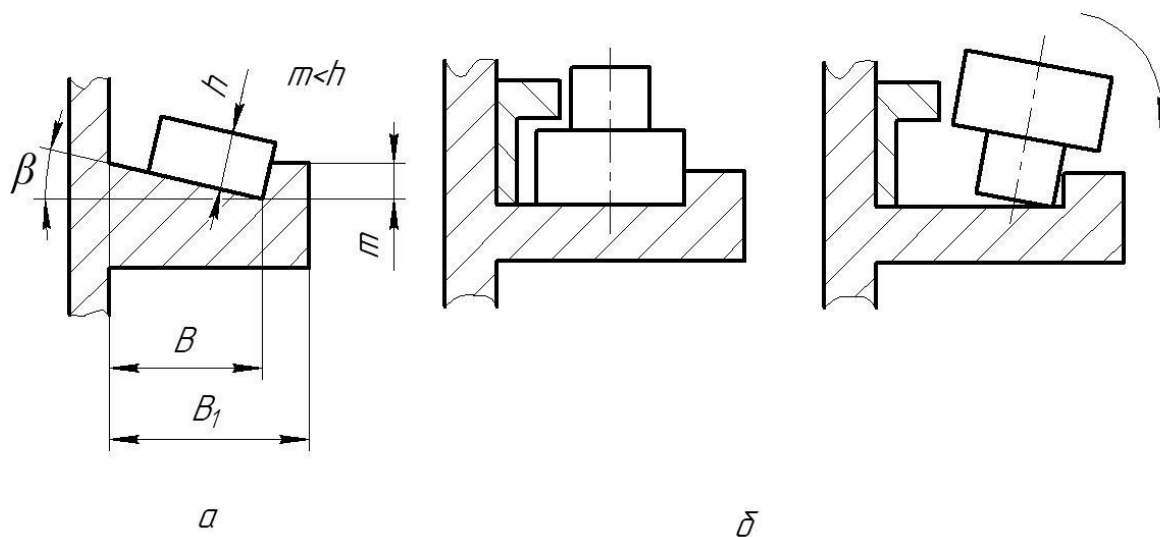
Способи орієнтування заготовок простої форми
